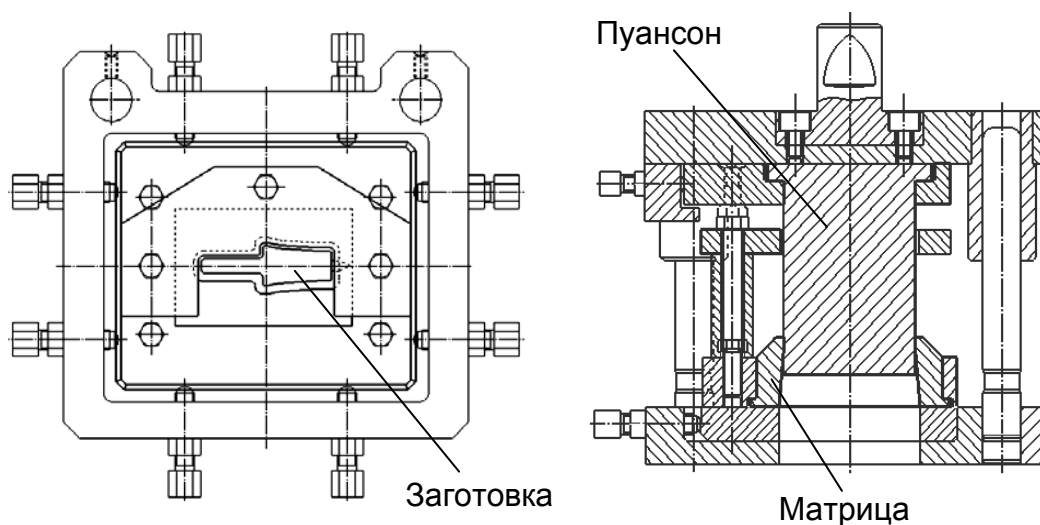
Эскиз обрезного штампа для обсечки обля поковки
